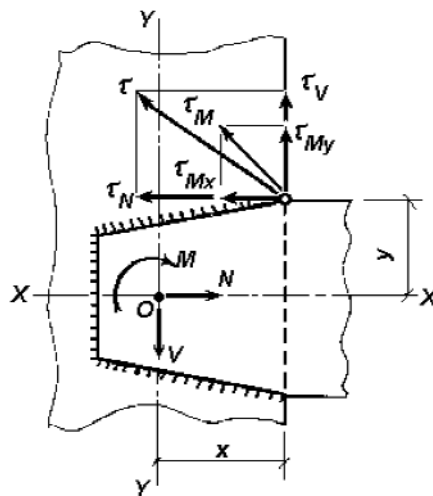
Розрахункова схема зварного з'єднання з кутовими швами
